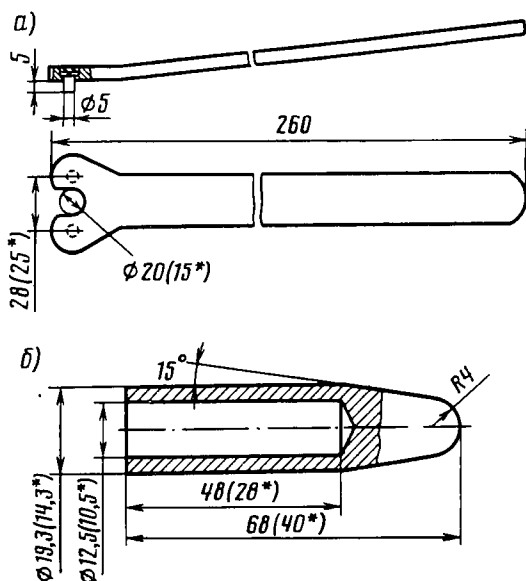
Инструмент и приспособление для амортизаторов передней и задней подвесок:
